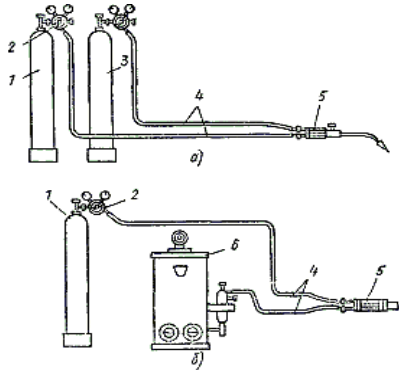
Схема газоживлення пересувного зварювального поста:
